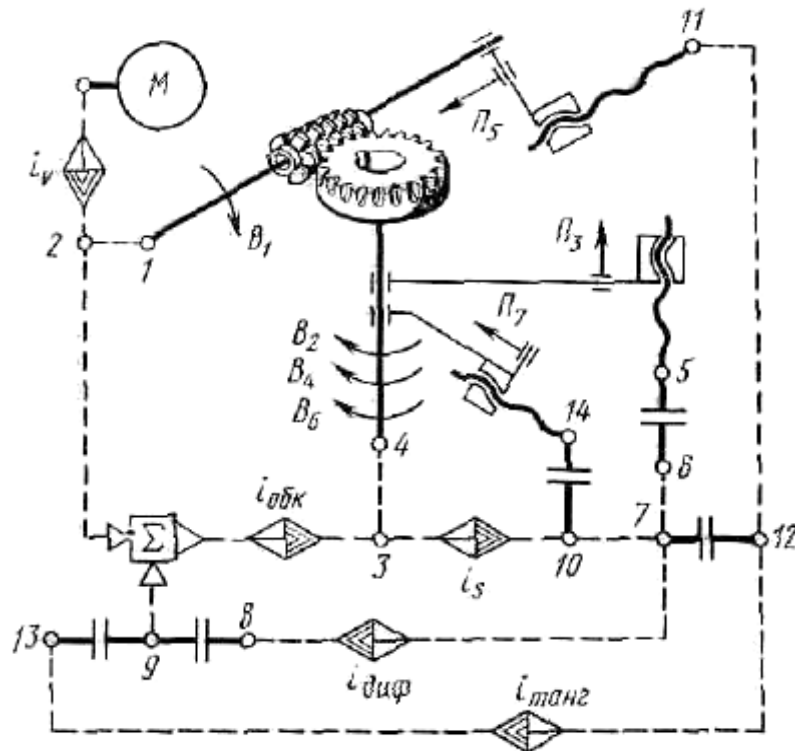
Структурная схема универсального зубофрезерного станка
